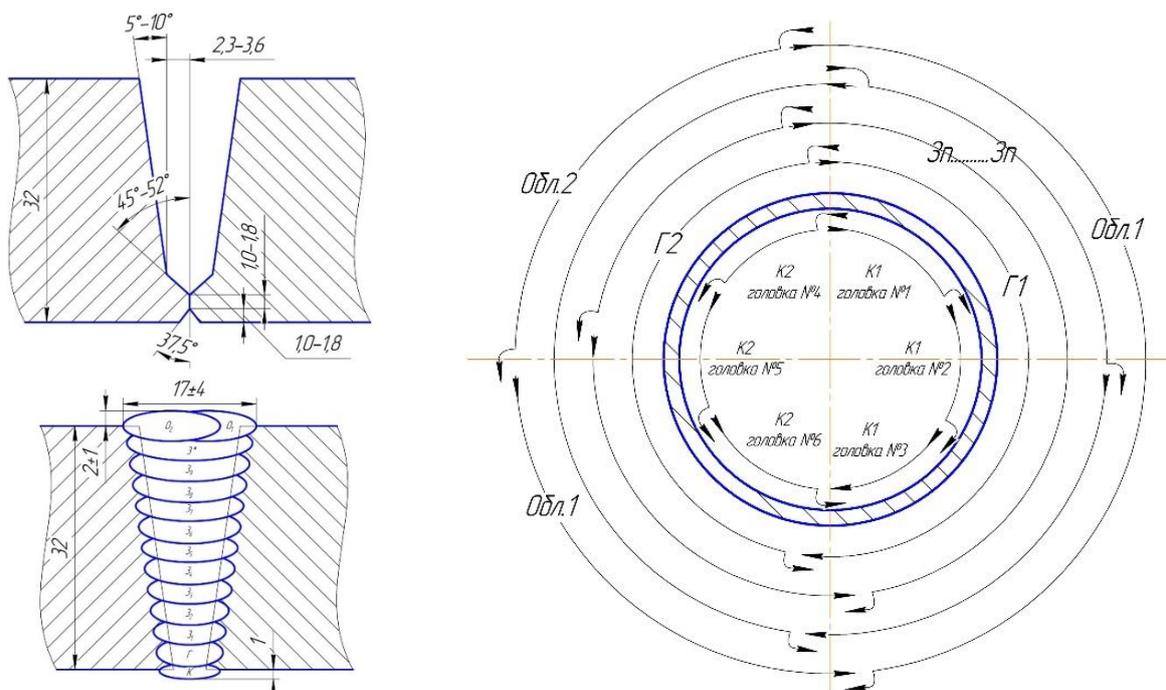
Геометрическая конструкция стыкового соединения для автоматической сварки в защитных газах. Для такой разделки кромок режимы дуговой сварки приведены в таблице 13;
